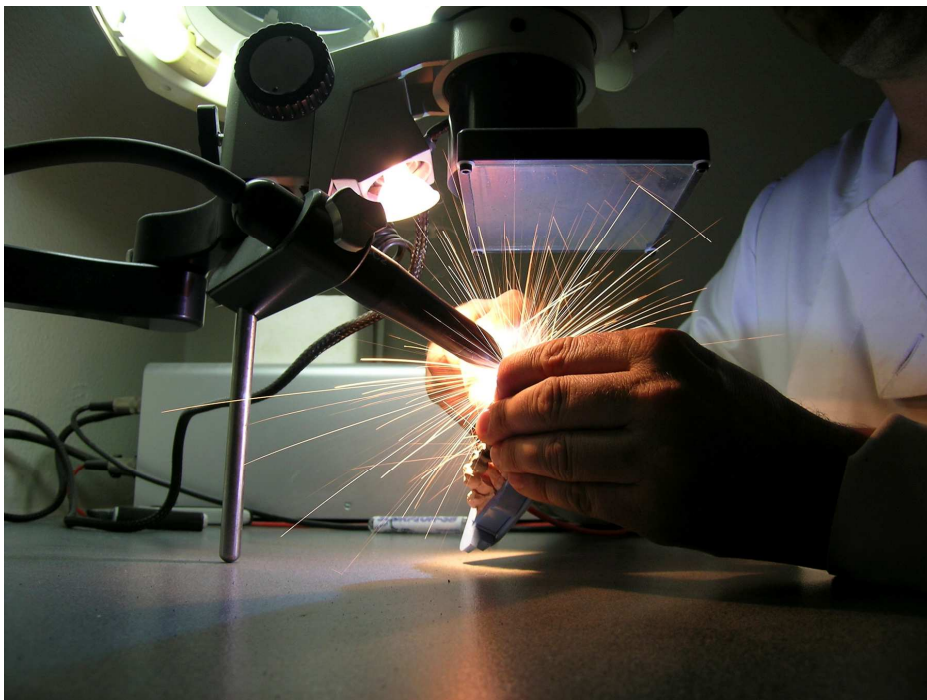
Soldadura de adición. Fuente: Migros dental S.A.
